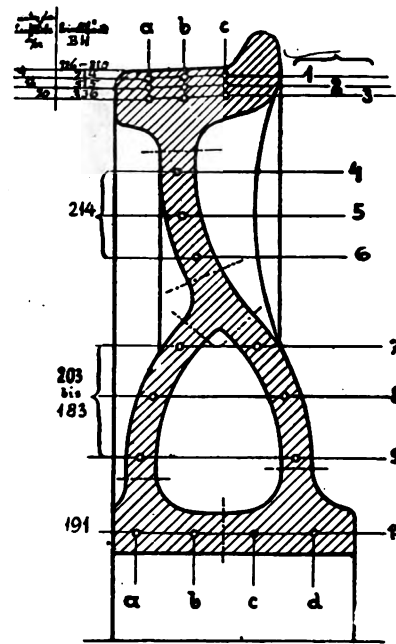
Querschnittsplatte aus einem Griffirad mit Lage der Prüfstellen für die Kugeldruckprobe.
